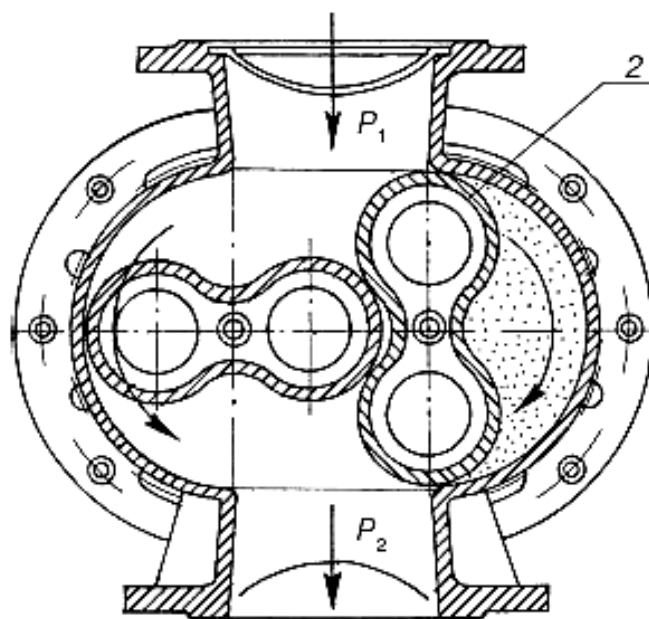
Схема роботи роторного лічильника газу: 1 – корпус; 2 – ротор
